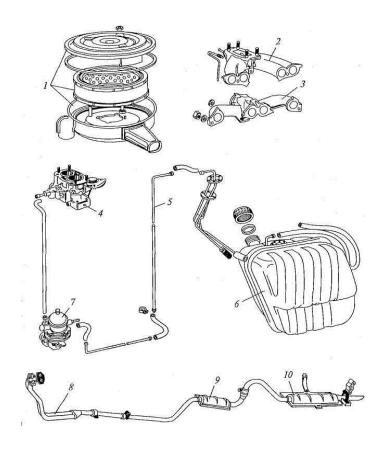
Система питания бензинового двигателя: 1 — воздушный фильтр; 2, 3 — трубопроводы; 4 — карбюратор; 5 — топливопровод; 6 — бак; 7 — насос; 8 — труба; 9, 10 — глушители
